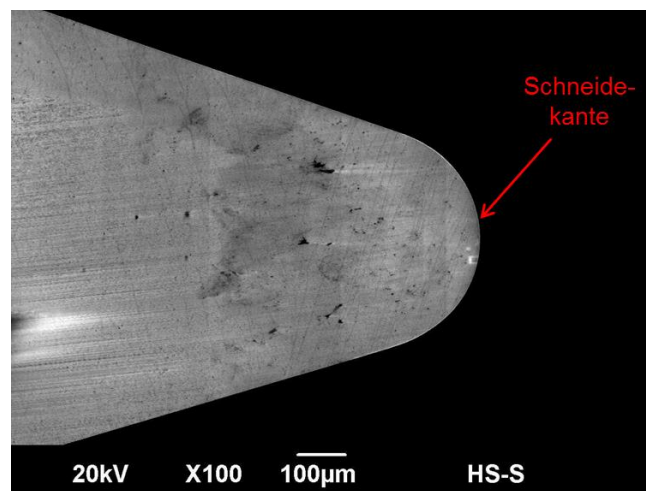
REM-Aufnahme einer binderlosen cBN-Schneide [63]
